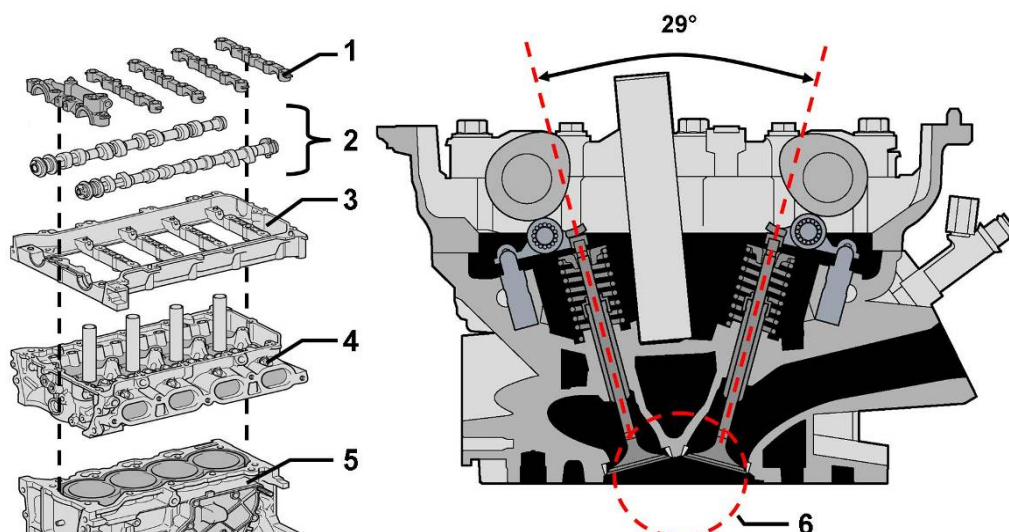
Основные элементы головки блока цилиндров: 1 - крышка подшипников; 2 - распределительные валы; 3 - картер распределительных валов; 4 - головка цилиндров; 5 - блок цилиндров; 6 - клиновидная камера сгорания
